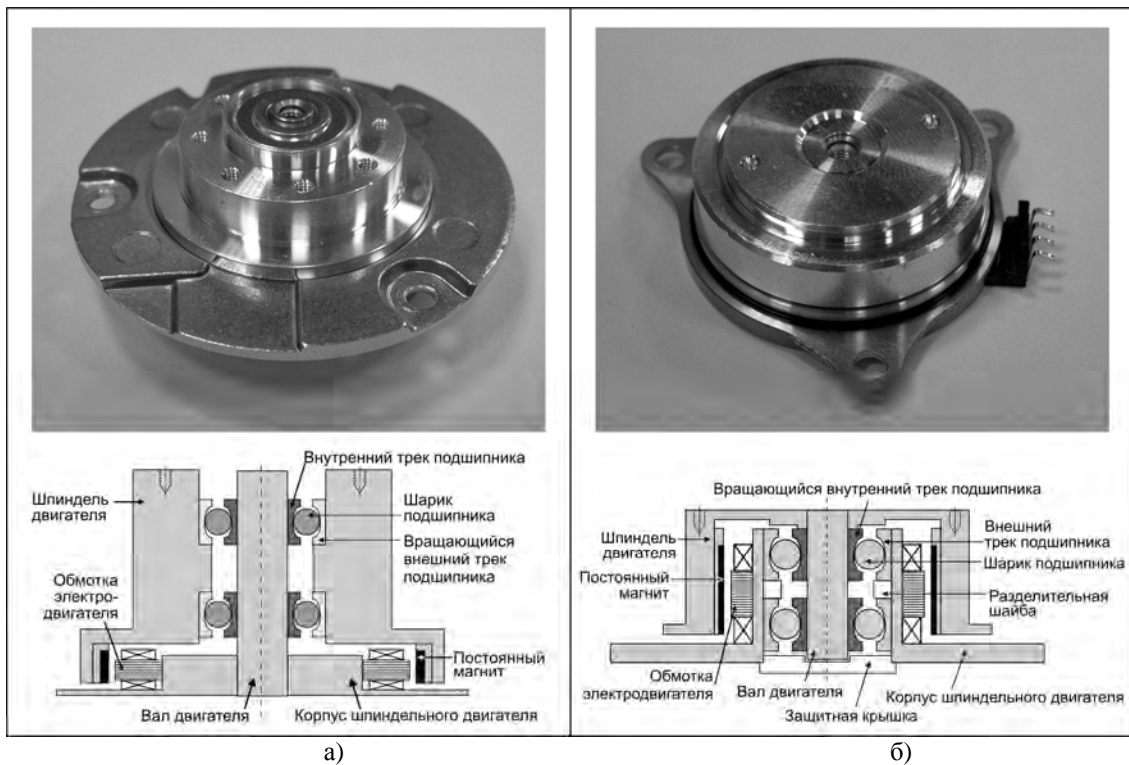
Внешний вид и схематическое изображение шпиндельных двигателей:
